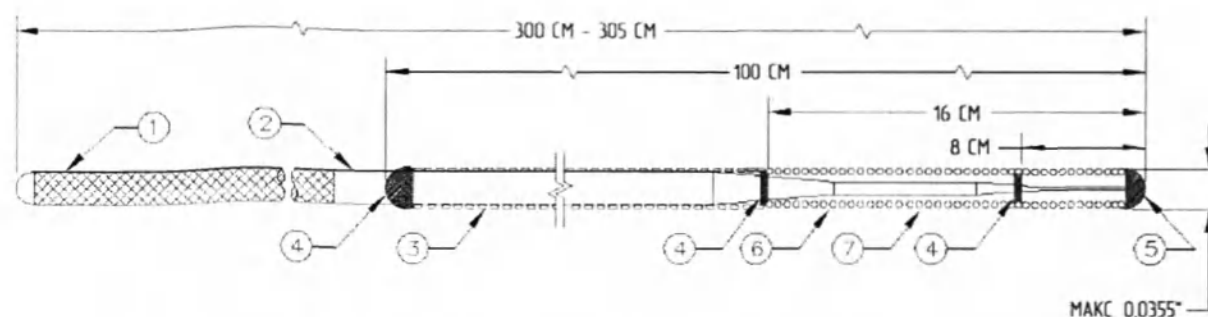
HI-TORQUE SUPRA CORE 35 (300 см, тип кончика - прямой)
